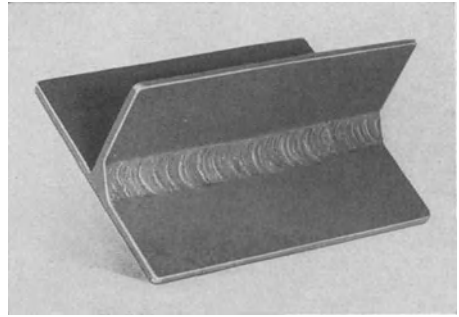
Arcatomgeschweißte Kehlnaht an Aluminiumblech.
